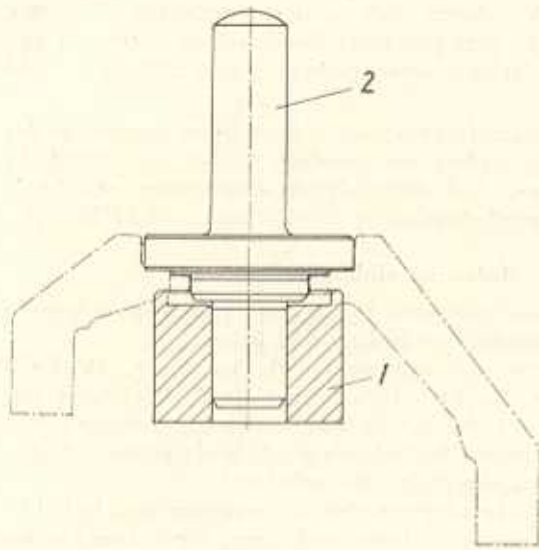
Einpreßvorrichtung für den Wellen-Dichtring in das Schwenklager (W-210 747)
